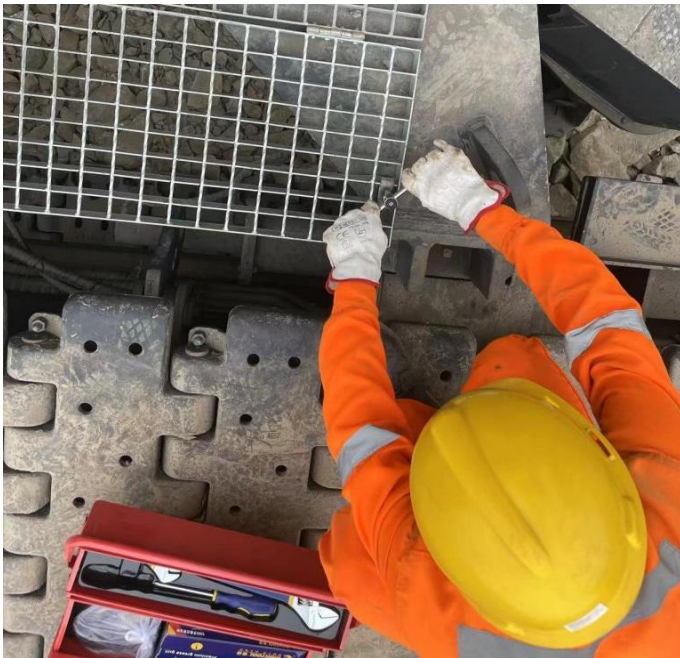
Anclado de la pista e instalación de la tubería de aceite 02.
